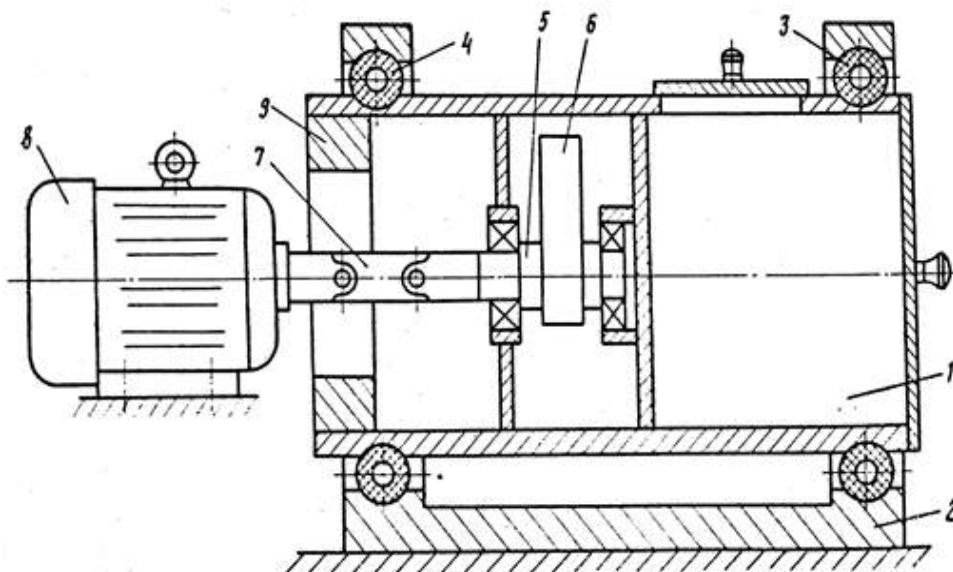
Пристрій для вібраційного зміцнення деталей: 1 – циліндрична робоча камера; 2 – основа; 3, 4 – тороподібні елементи; 5 – вал; 6 – дебаланс; 7 – муфта; 8 – електродвигун; 9 – противага
